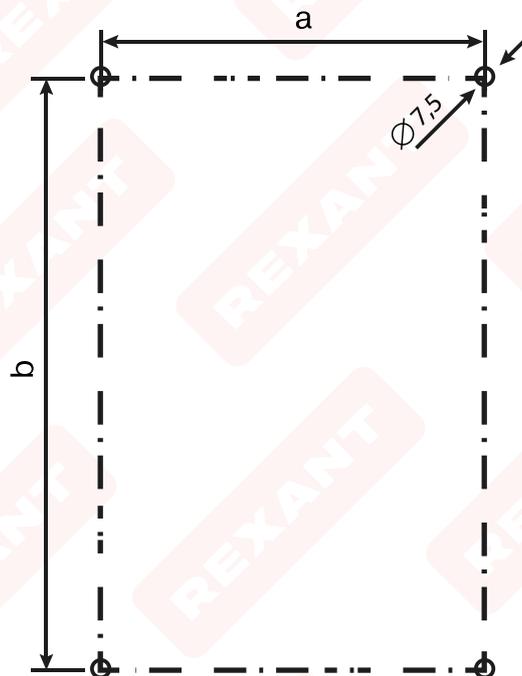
Установочные размеры корпусов с пластиковыми кронштейнами для крепления к стене
